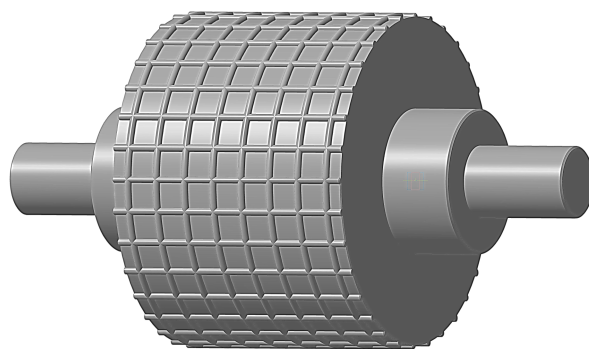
Трёхмерная модель рифлёного валка с наплавленной сеткой на рабочей поверхности бандажа
